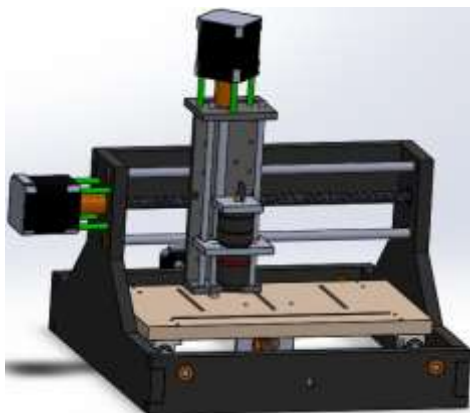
Ensamblaje completo del mecanismo de posicionamiento.
